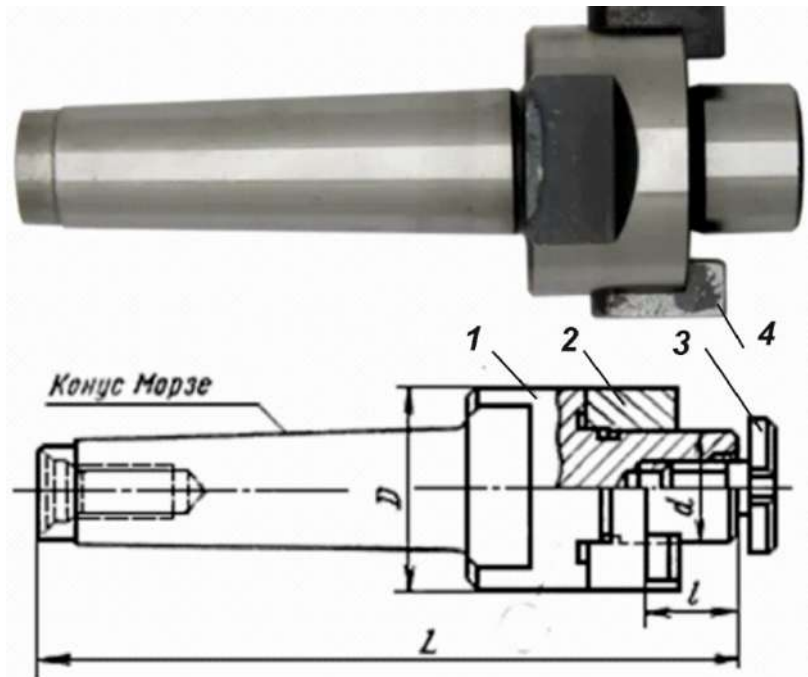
Кріплення насадної фрези за допомогою гвинта
